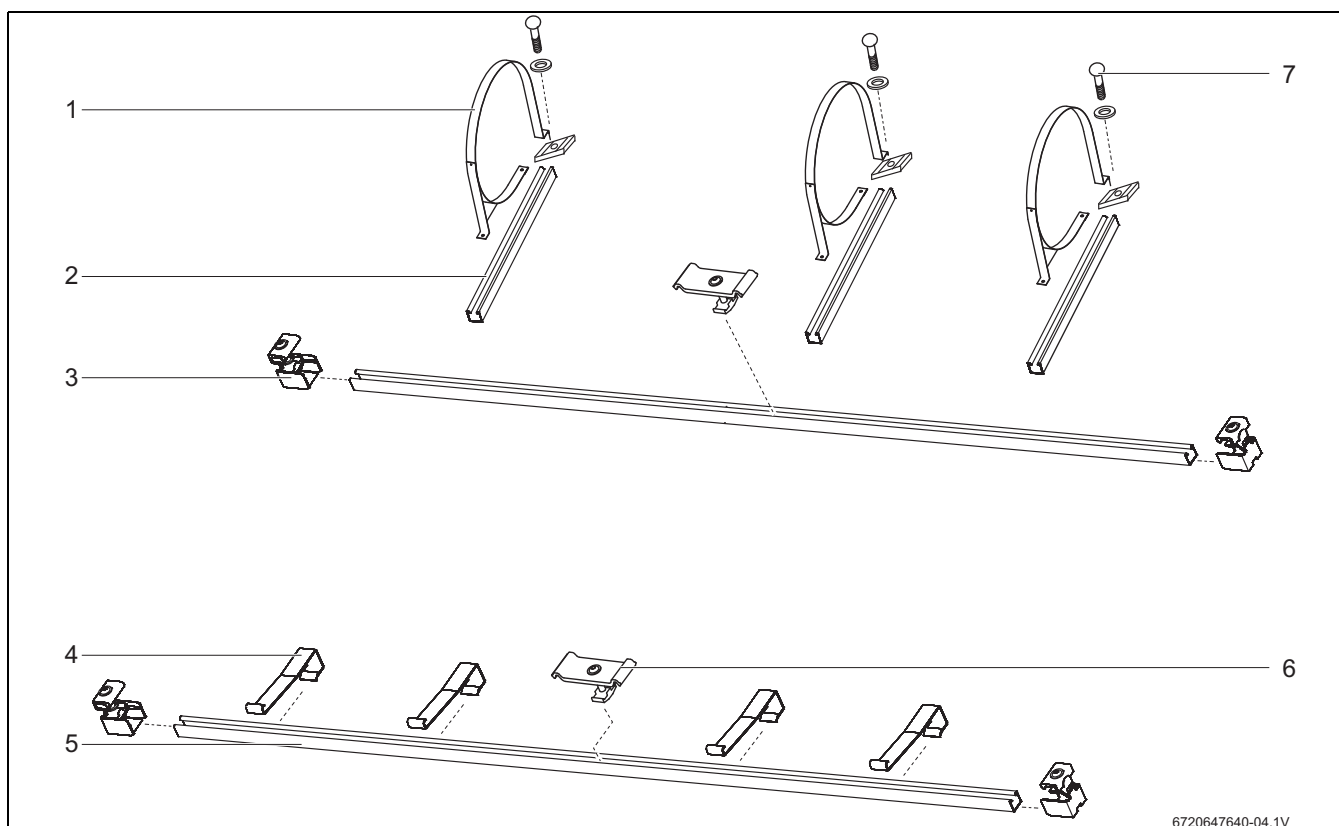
Juegos de montaje para 2 captadores: 1 juego de soporte básico, 1 juego de soporte adicional
